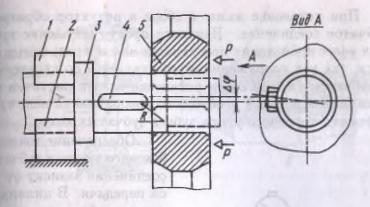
Схема установки зубчатого колеса на вал: 1 — прижимная призма; 2 — опорная призма; 3 — вал; 4 — шпонка; 5 — зубчатое колесо
